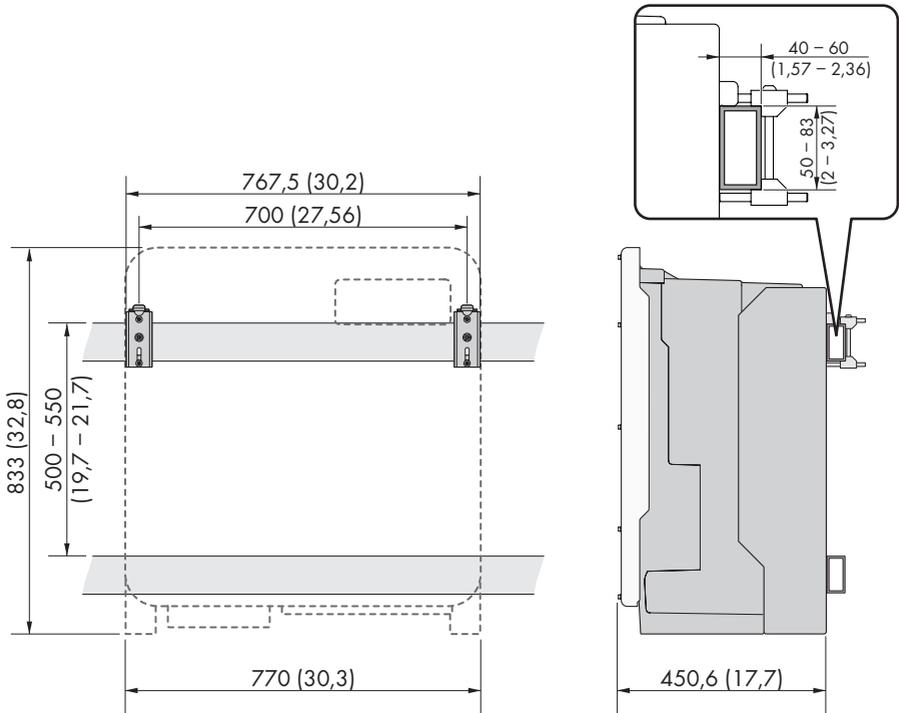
Dimensionado de los carriles perfilados y zona de apriete del soporte de montaje (medidas en mm [in])
